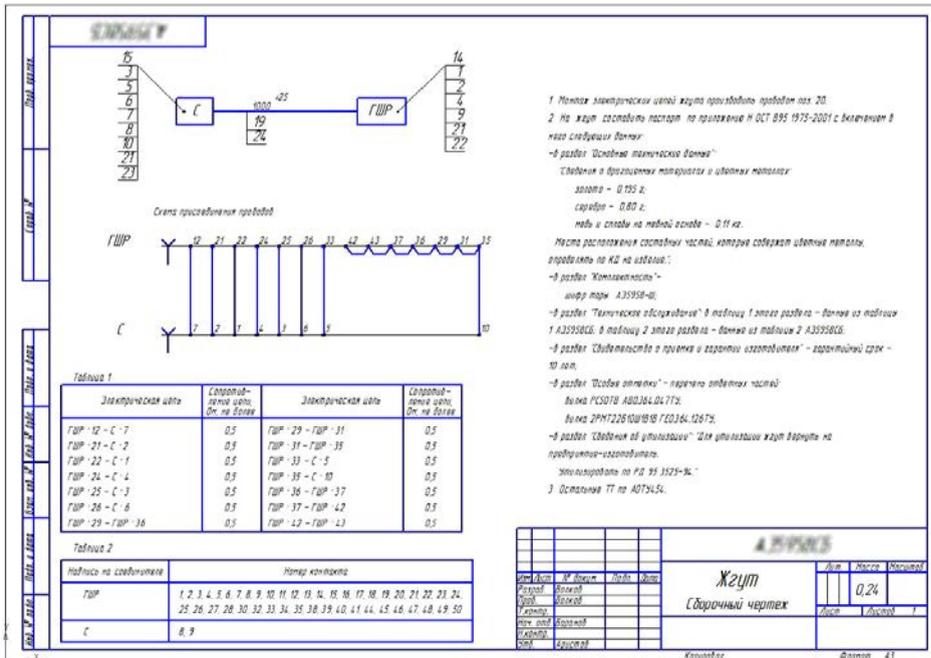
Сборочный чертеж жгута, скомпонованный в КОМПАС-3D
